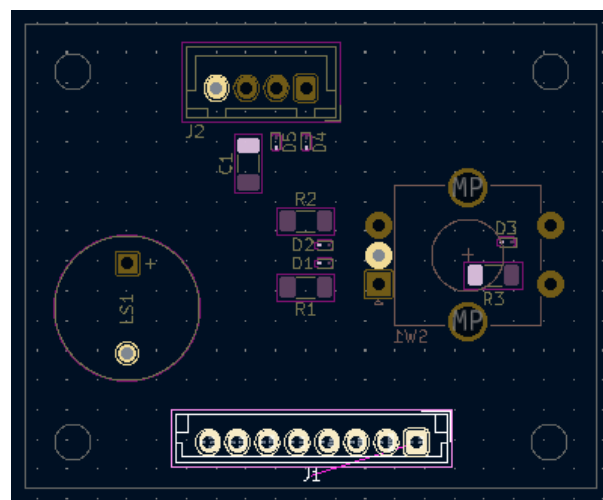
Subsistema Conector Placa Principal en PCB Interfaz
